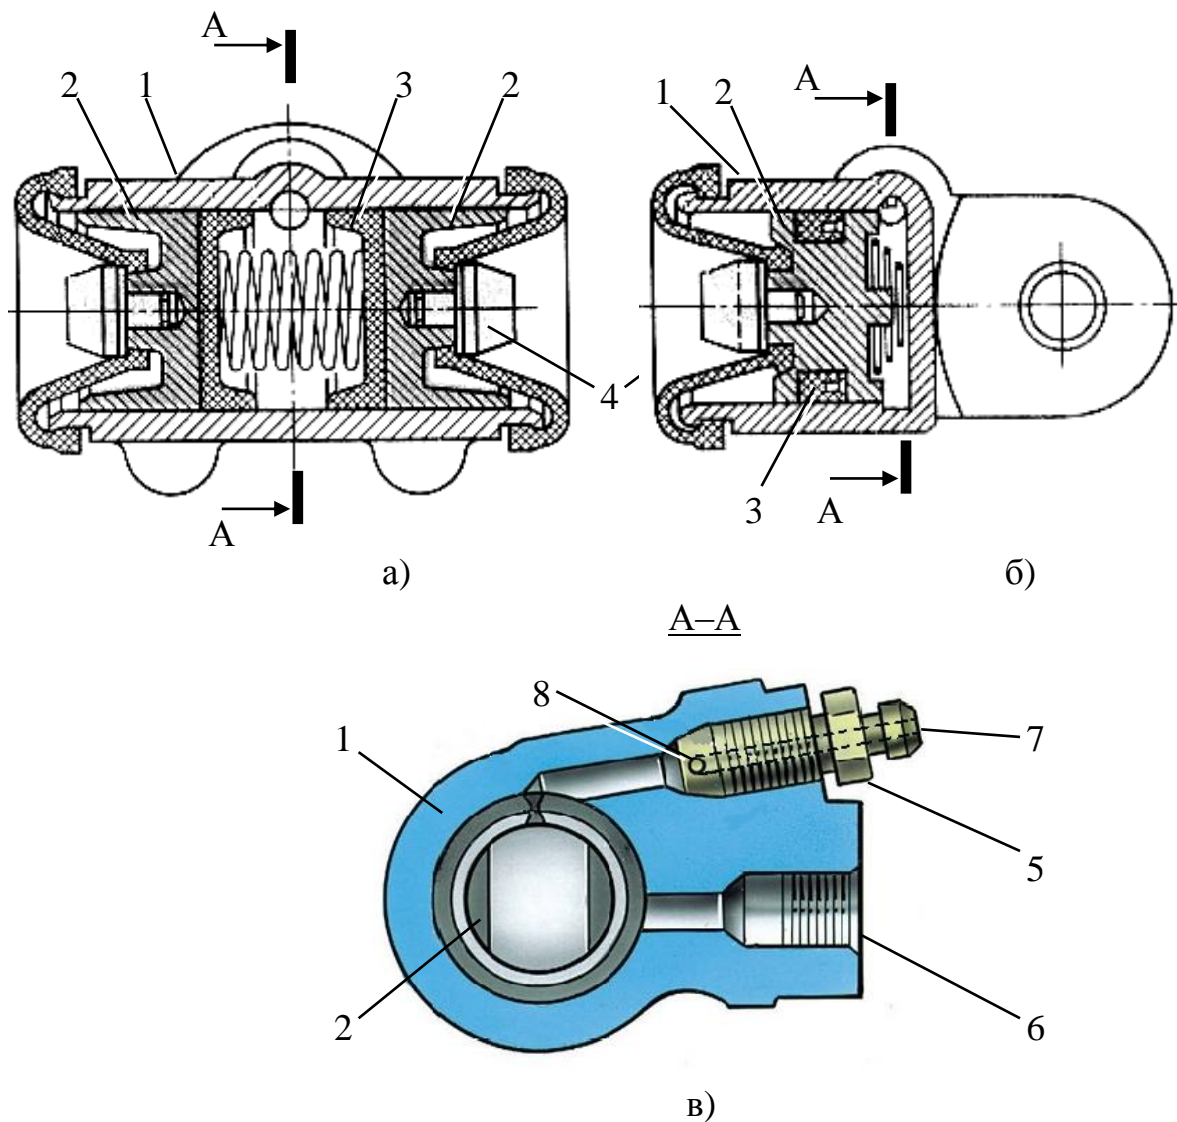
Конструкция рабочих цилиндров: а – с двумя поршнями, б – с одним поршнем; 1 – корпус рабочего тормозного цилиндра; 2 – поршни; 3 – уплотняющие манжеты; 4 – упоры тормозных колодок; 5 – штуцер выпуска воздуха; 6 – подводящее отверстие; 7 – центральное отверстие штуцера; 8 – боковое отверстие штуцера
